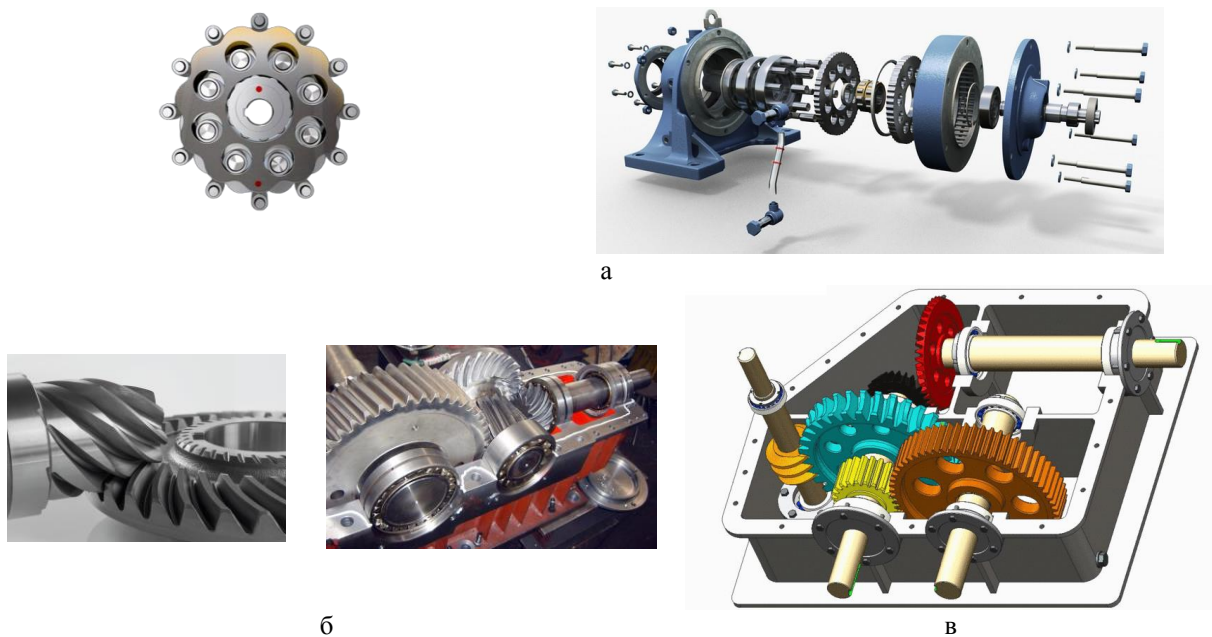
Комбіновані типи редукторів: а – хвильовий редуктор, вісі співвісні; б – гепоїдний редуктор, комбінована схема розташуванні вісей; в – комбінований редуктор, комбінована схема розташуванні вісей
